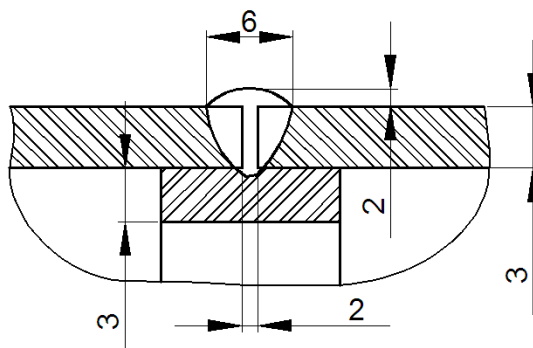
Схема з'єднання С4 обичайки ресивера
